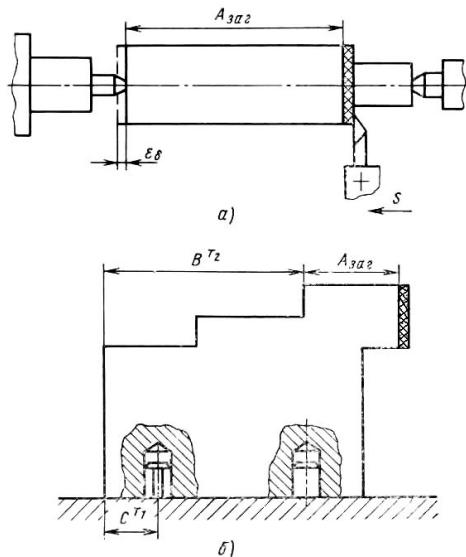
Примеры несовпадения технологической и измерительной баз, вызывающие погрешность базирования при настроенном на размер инструменте
